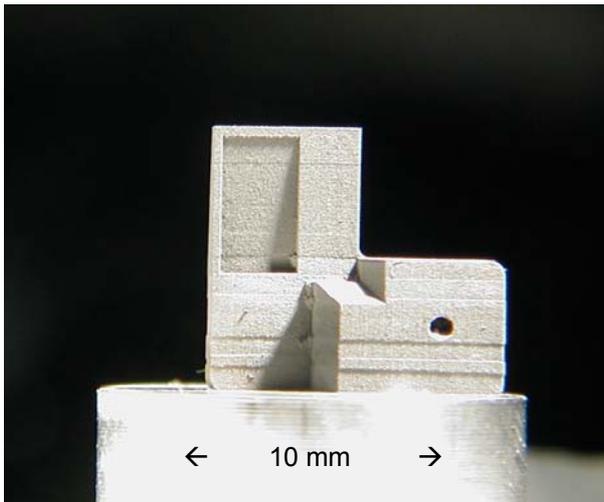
Bauteil aus Wolfram mit innerer Struktur
